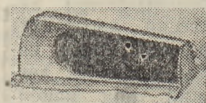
Ведущая шестерня. Расположение контакта одинаково для обеих сторон зуба.
